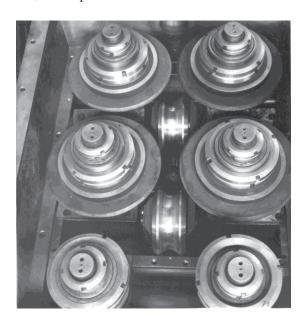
Внешний вид опорно-сварочного узла ТЭСА АДС
